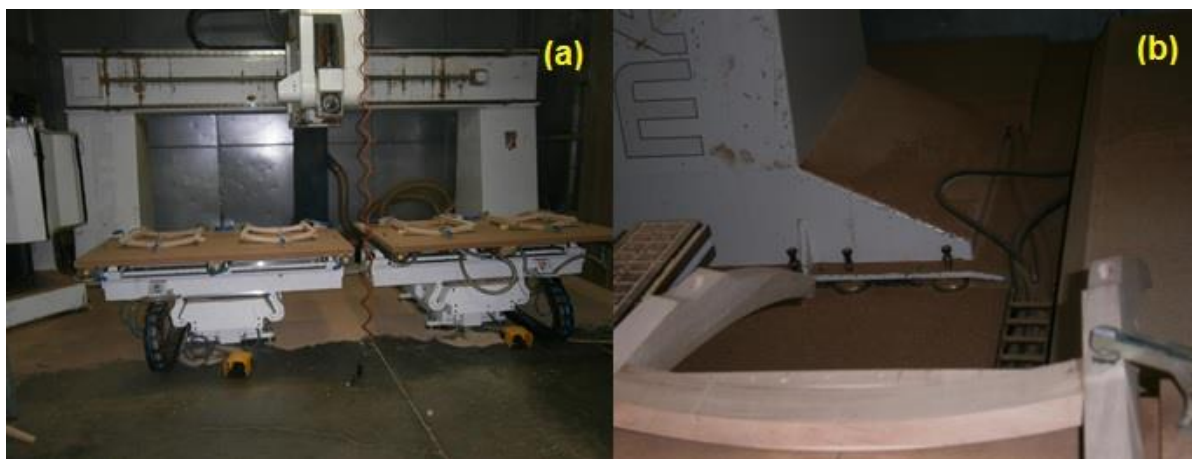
Geração da serragem. (a) Centro de usinagem, (b) serragem entorno da maquina.
